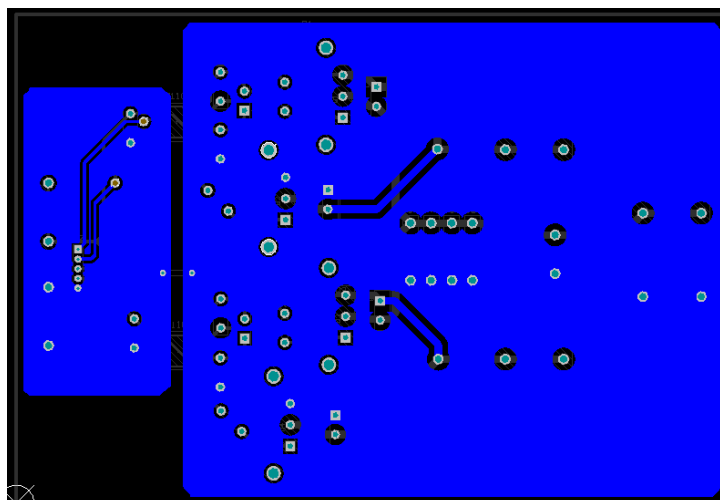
Layout capa BOTTOM de primer prototipo del inversor
